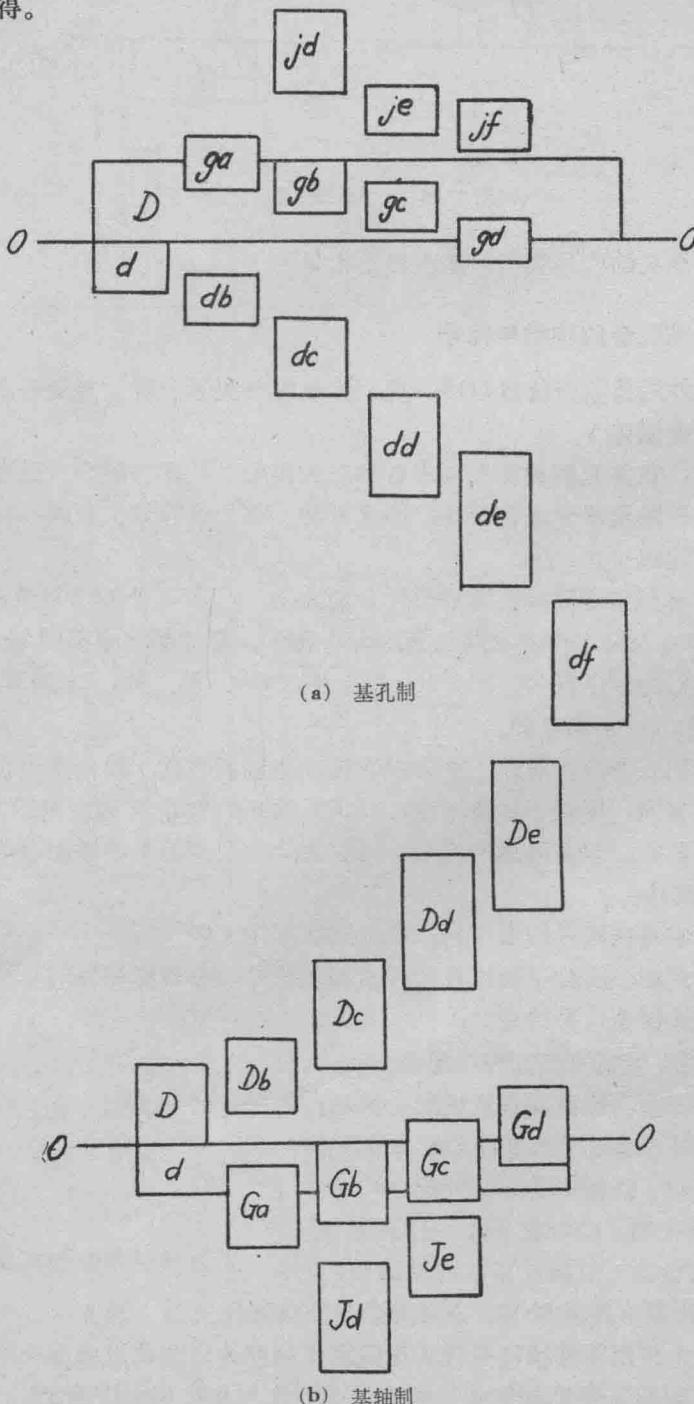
2 级精度标准配合的公差带图 (尺寸 1~500 mm)
